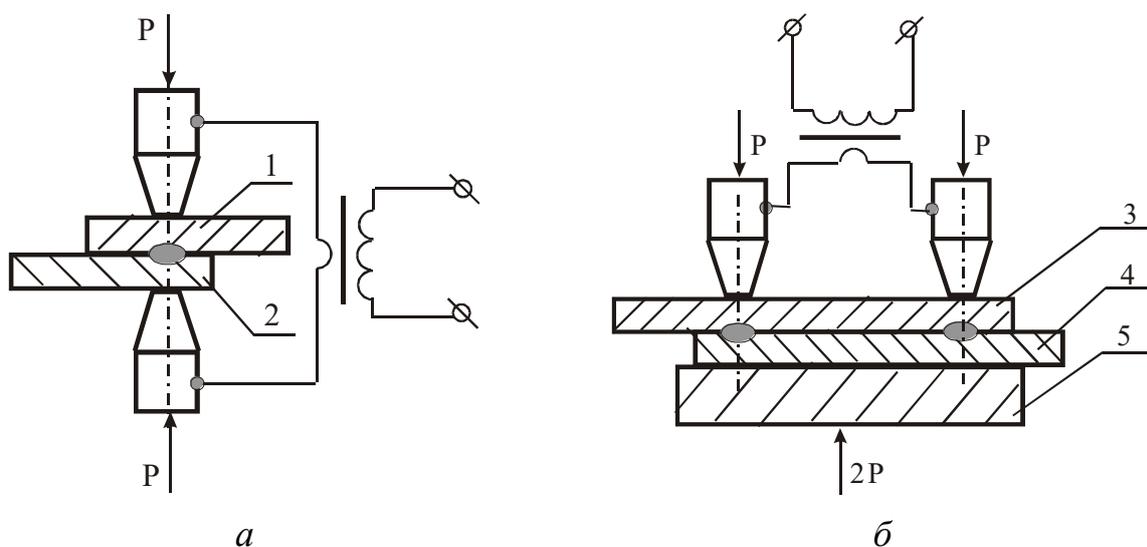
Схема контактної точкової зварювання дво- (а) і одностороннього (б)
